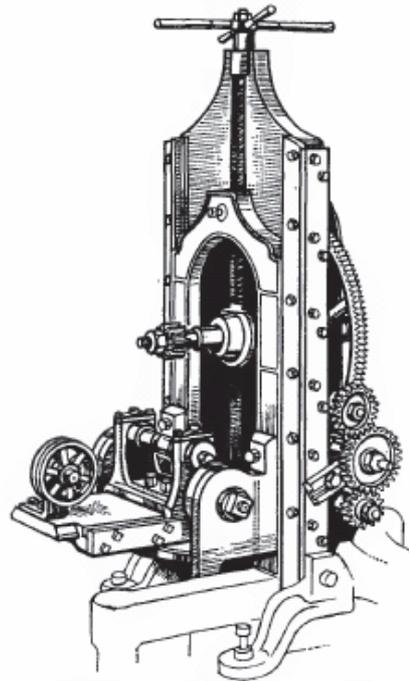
Máquina cortadora de engranes desarrollada por Richard Roberts en 1821.
